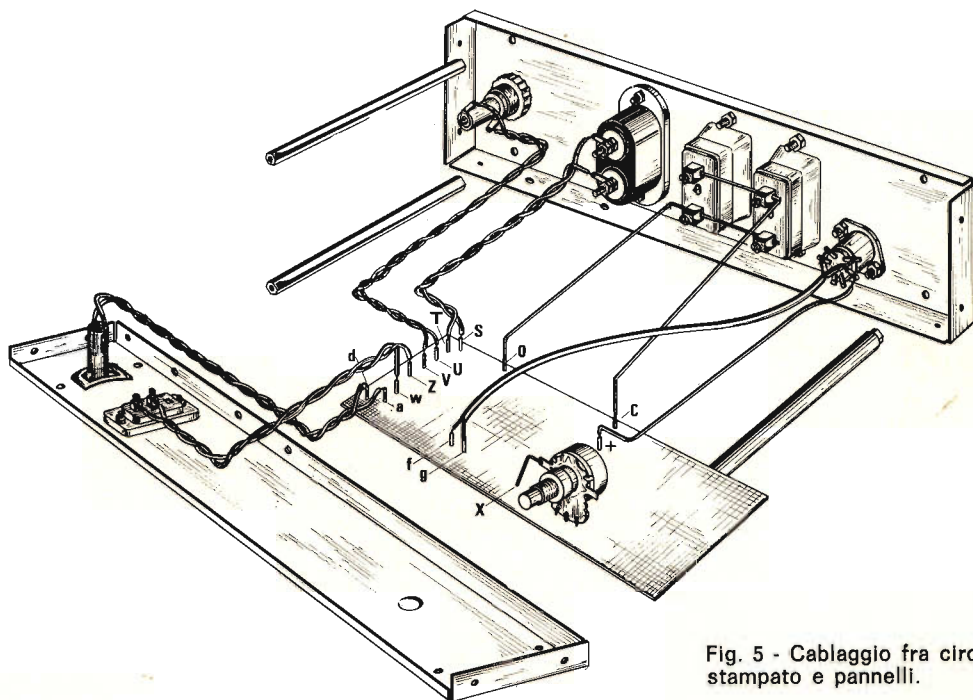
Cablaggio fra circuito stampato e pannelli.
